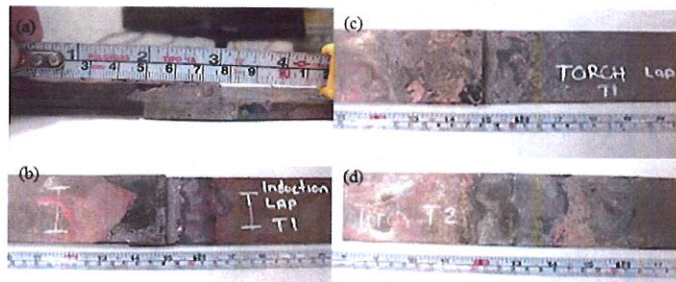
Uniones realizadas por soldadura Fuerte en cobre electrolítico a) Configuración del área de contacto de la junta en traslape, b) Aspecto visual de la unión a traslape por inducción c) Vista superior de la junta a traslape realizada por antorcha y d) Aspecto de la junta a tope realizada por antorcha.
